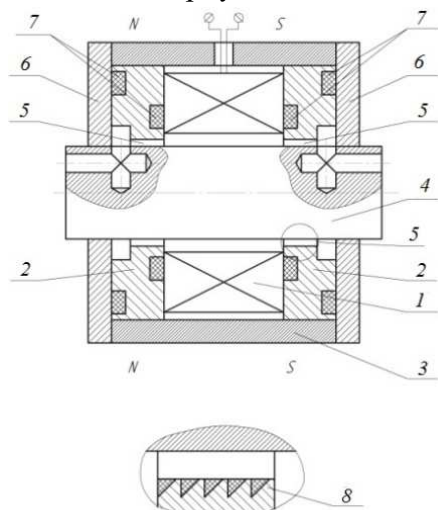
Схема магнитореологического дросселя: 1 – катушка, 2,3,4 – магнитопровод, 5 – рабочий зазор с МРЖ, 6 – корпус, 7 – уплотнения, 8 – концентраторы магнитного поля
